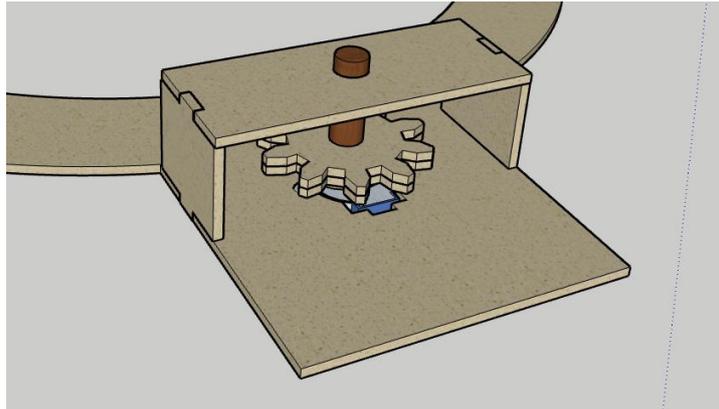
Engrenagem encaixada no eixo do motor sobre a estrutura formada pelas peças 16, 18 e 20 coladas.
